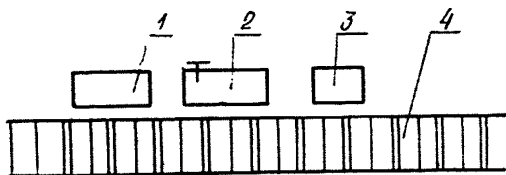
Типовая схема планировки рабочего места разборки коробки передач
